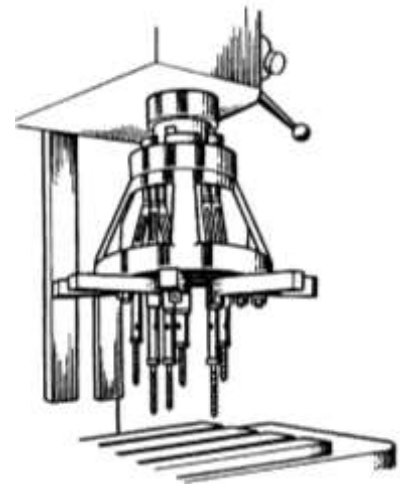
Багатошпindelна головка, яка переналагоджується [39].
